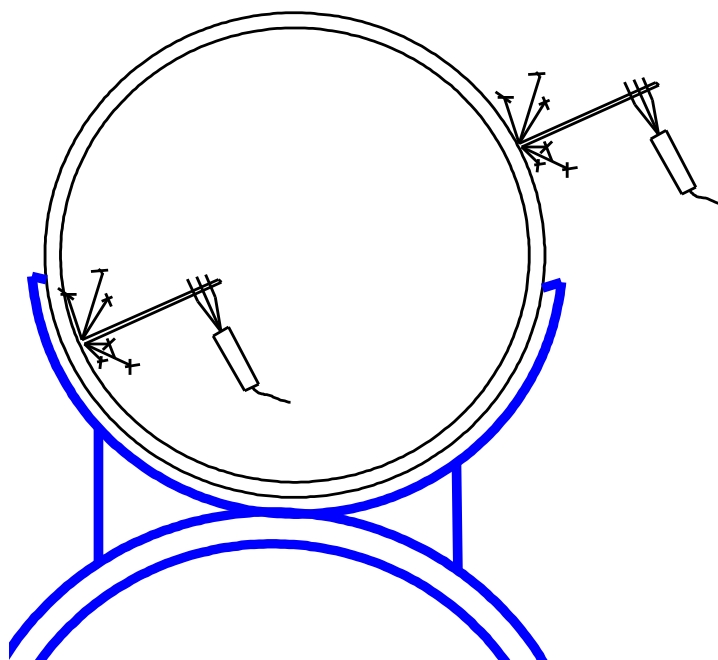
Сварка корневого слоя шва
